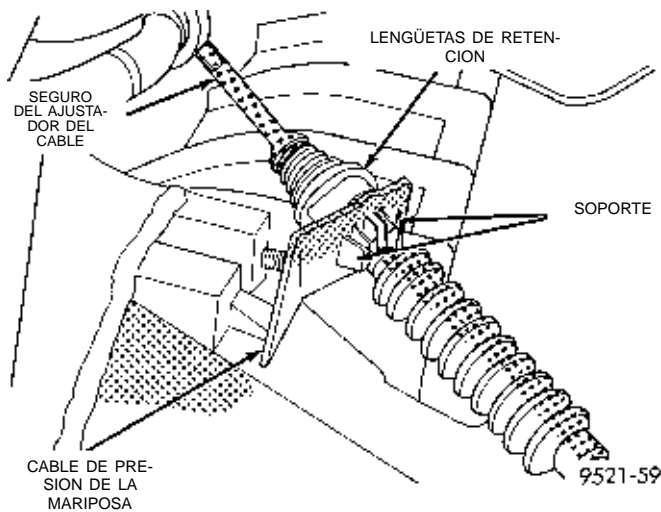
Soporte del cable de presión de la mariposa del acelerador
